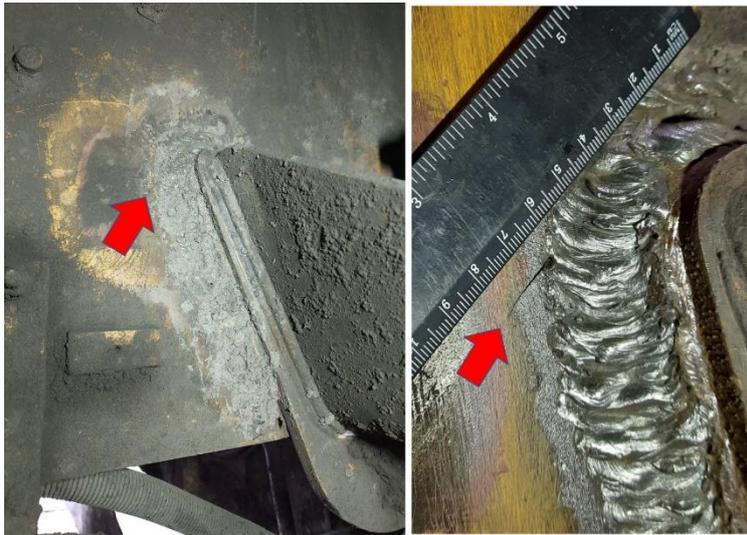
Дефект в сварном шве опоры двигателя (датчик № 12)
